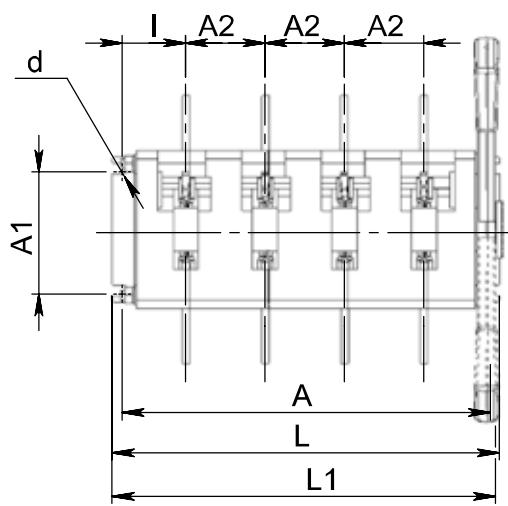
Выключатель-разъединитель на одно направление 4-полюсный с боковой рукояткой
